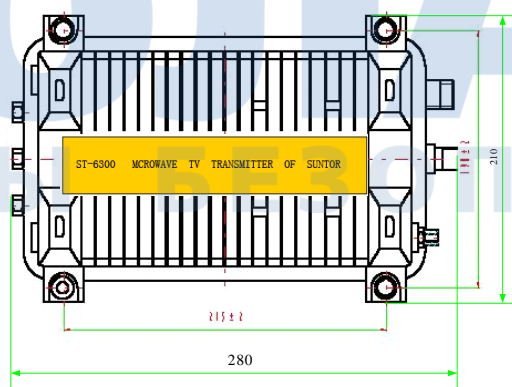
Внешний вид и размеры передатчика WS-0902/1013.
